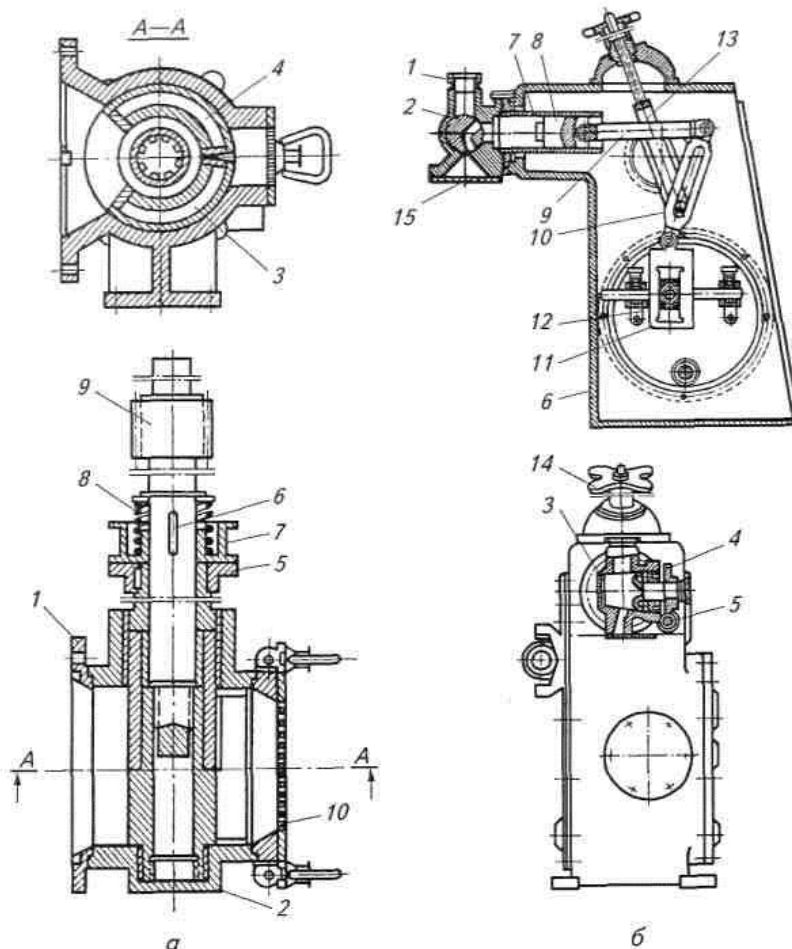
Дозаторы: *а* — обезжиренного творога: 1 — корпус; 2 — съемная крышка; 3, 4 — рабочие секторы; 5 — полумуфта; 6 — направляющая шпонка; 7 — муфта; 8 — пружина; 9 — шестерня; 10 — решетка; *б* — сливок: 1 — патрубок; 2 — корпус крышки; 3 — поворотный кран; 4 — шестерня; 5 — зубчатая рейка; 6 — корпус дозатора; 7 — цилиндр; 8 — поршень; 9 — тяга; 10 — пазовый рычаг; 11 — кулиса; 12 — ползун; 13 — резьбовая тяга; 14 — вороток; 15 — решетка
